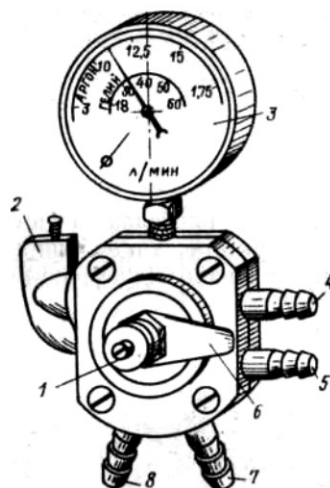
Расходомер регулятор редукторного типа без блокировки сварочного тока по воде и газу
